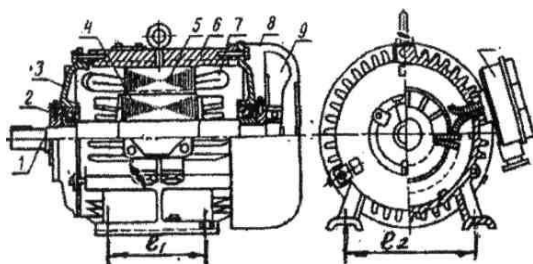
Двигатель асинхронный, трехфазный с коротко замкнутым ротором: 1 - вал ротора; 2 - подшипник; 3 - подшипниковый щит; 4 - сердечник ротора; 5 – сердечник статора; 6 - корпус; 7 - обмотка; 8 - кожух вентилятора; 9 - вентилятор; 10 - коробка выводов; размеры L_1 и L_2 – продольное и поперечное расстояния между отверстиями в лапах а также двигатель постоянного тока - рабочая машина; основание для их крепления; муфта для соединения папок машин; мегомметр; инструменты.
